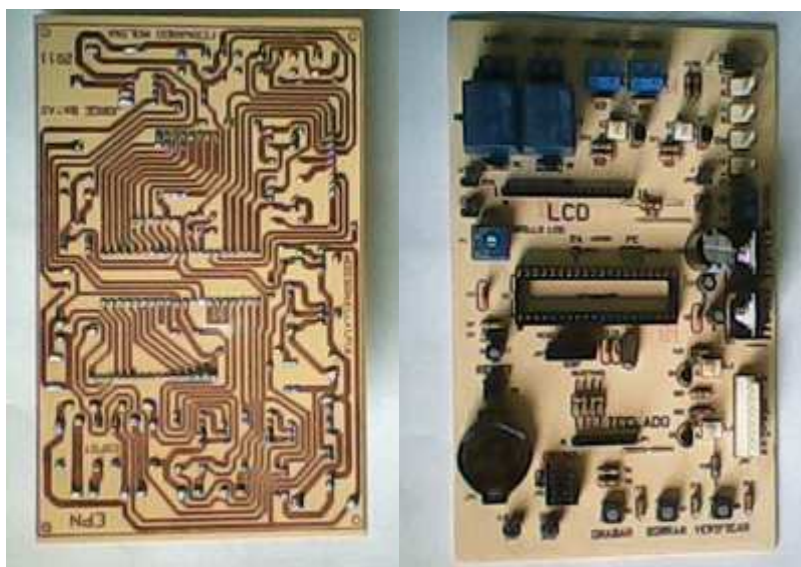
“Elementos Soldados en la Placa”
